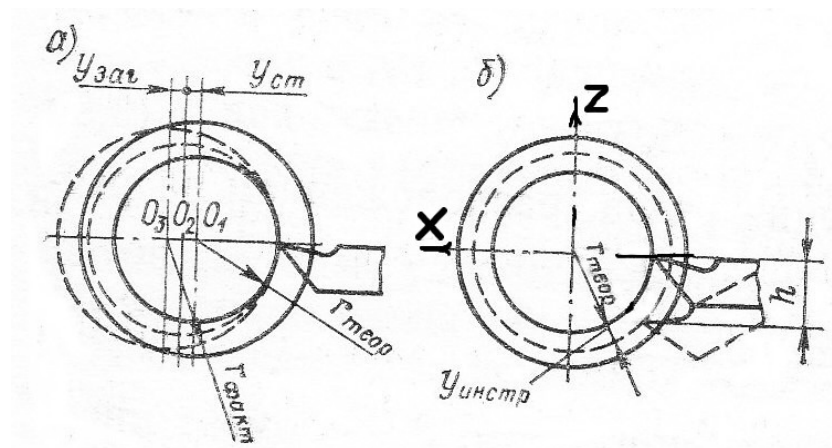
Влияние упругих отжатию на размер обрабатываемой заготовки
